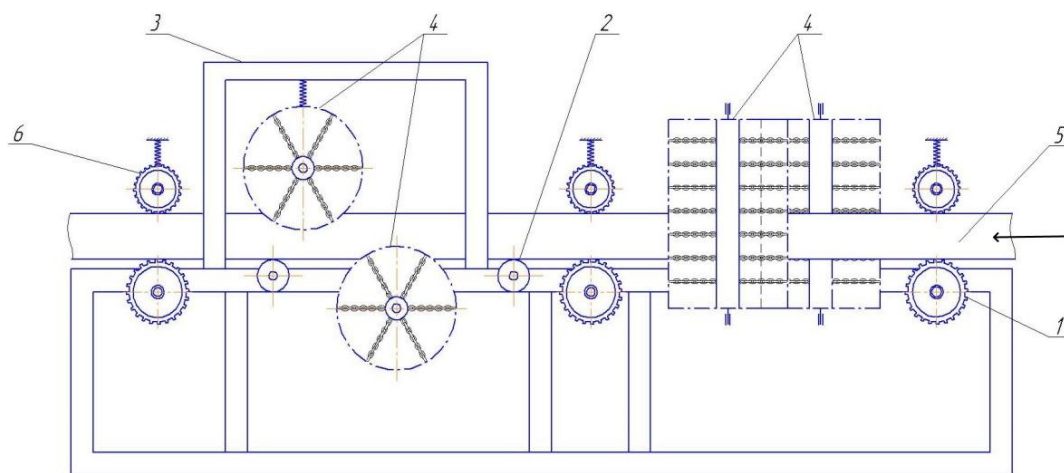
Вид с боку окорочного станка с ЦРО для обработки тонкомерных лесоматериалов: 1 – нижний приводной валец системы подачи; 2 – поддерживающий ролик; 3 - рама; 4 – горизонтальные и вертикальные пары цеповых валов; 5 – обрабатываемый ствол дерева; 6 – верхний прижимной валец
